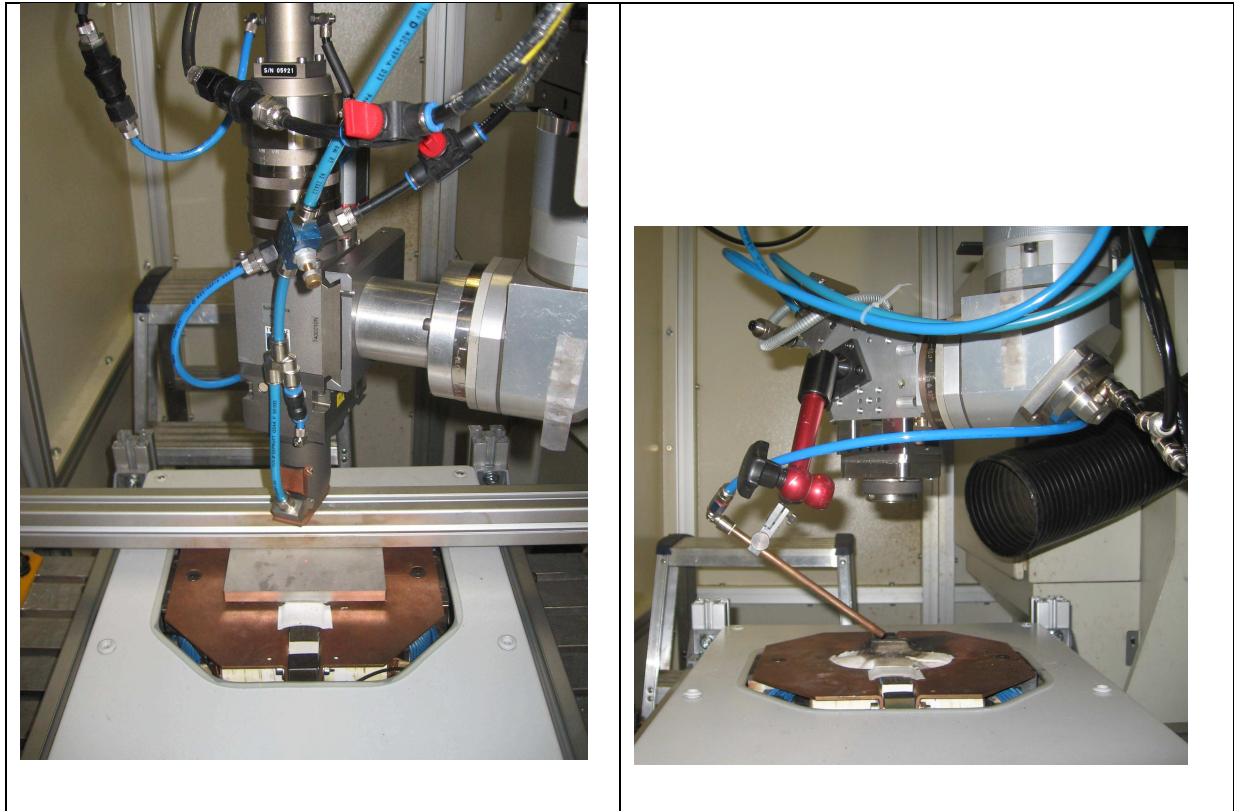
Versuchsaufbau links: Bearbeitungskopf des Festkörperlaseres mit Werkstück und Magnet; rechts: Bearbeitungskopf des CO₂-Lasers mit Magnet, beim Schweißen mit CO₂-Laser wurde ergänzend Schutzgas eingesetzt
